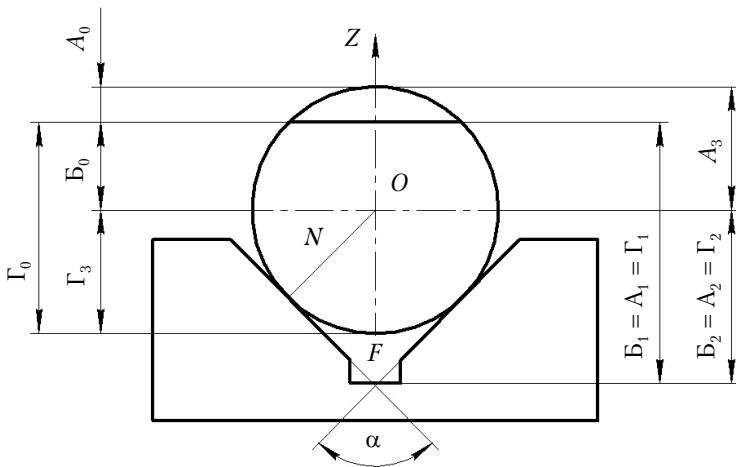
Образование погрешности размера расположения лыски в направлении оси Z при установке заготовки на призму
